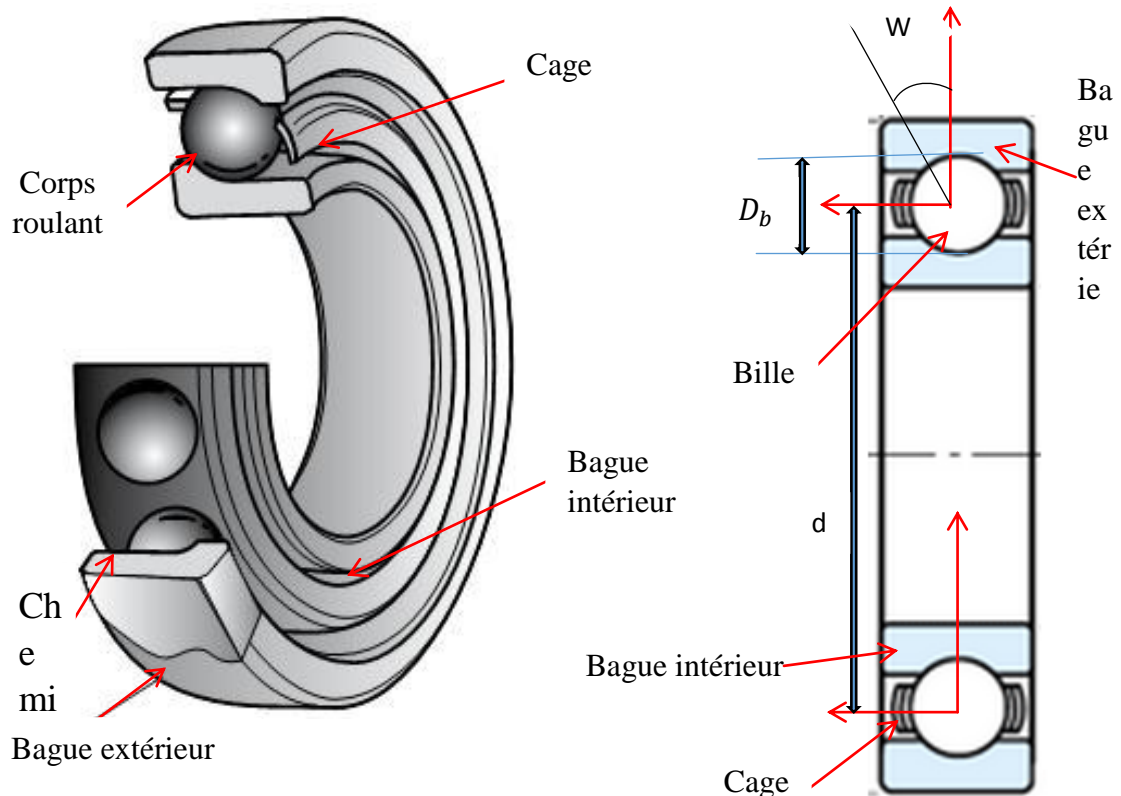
Vue éclatée des éléments constitutifs et Dimensions d'un roulement à billes
